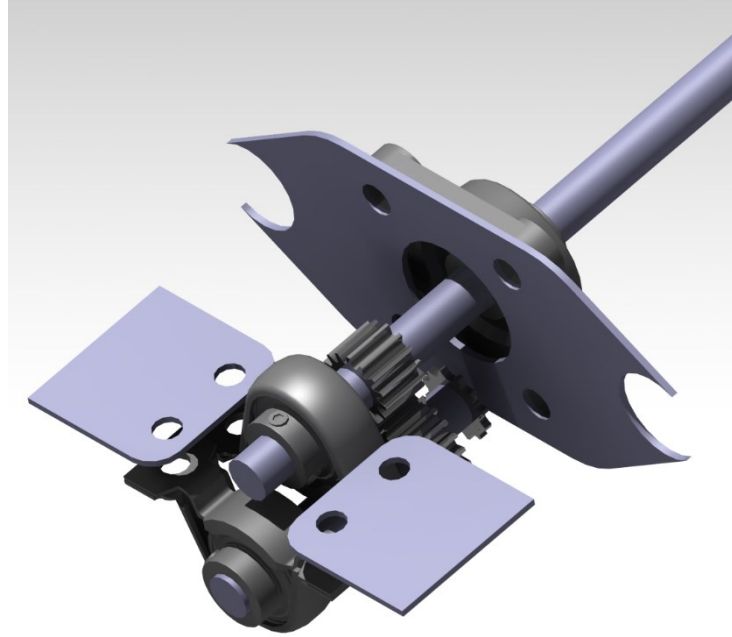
Montagem da caixa de direção. Fonte: Elaborado pelo autor em conjunto da equipe de *package*.
